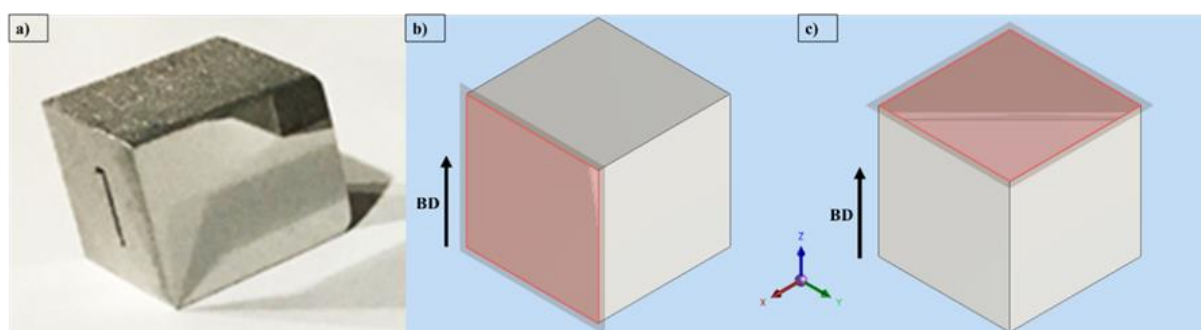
Geometria das amostras e planos de referência para as análises, a) cubo fabricado por LPBF, b) plano paralelo a direção de construção e c) plano perpendicular a direção de construção.
